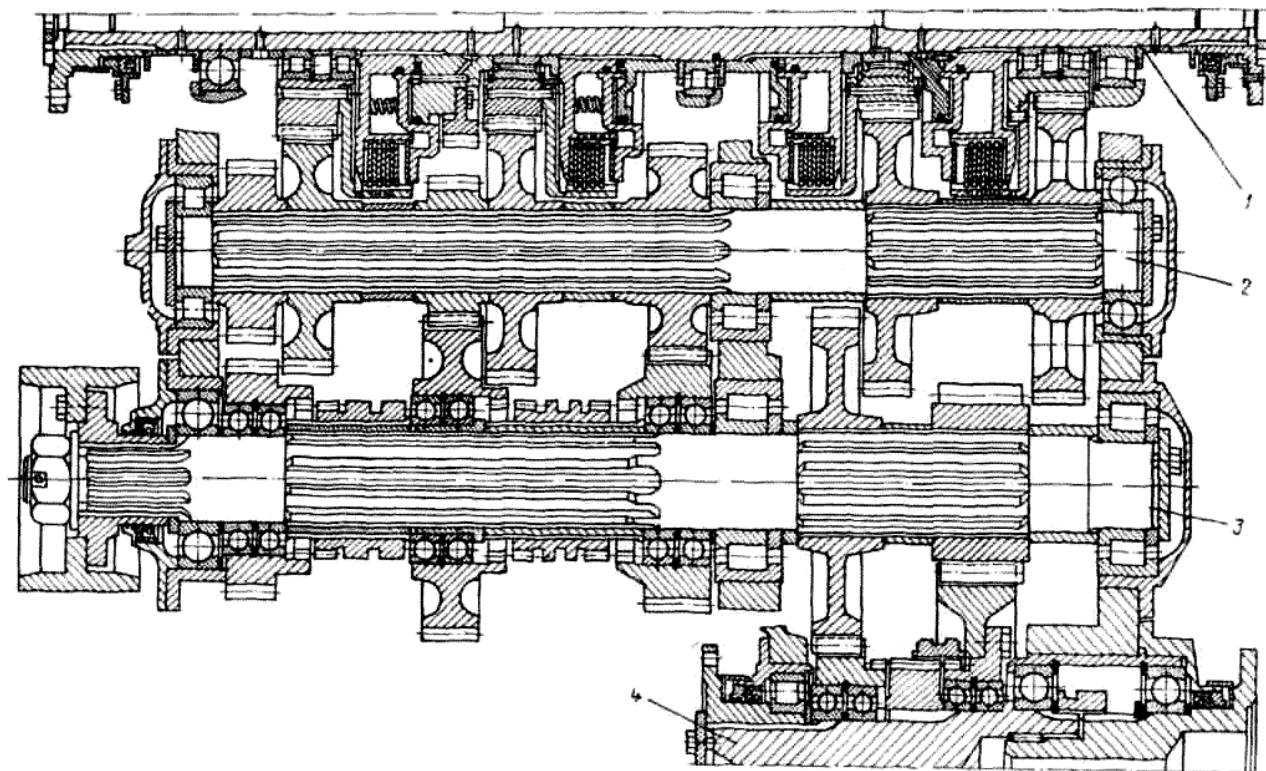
Конструкция коробки передач с индивидуальными фрикционными
